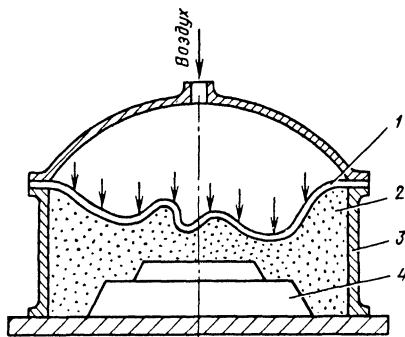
Схема прессования смеси гибкой диафрагмой:
